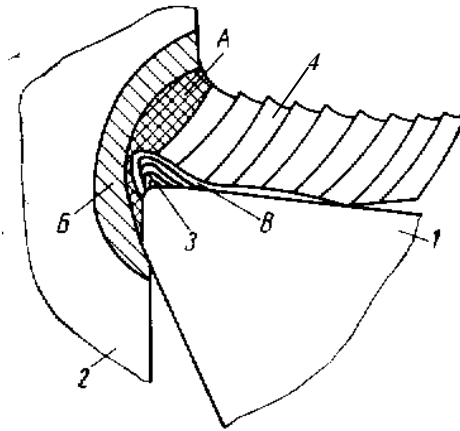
Схема зоны стружкообразования при резании материалов: 1 – инструмент; 2 – заготовка; 3 – нарост; 4 – стружка
